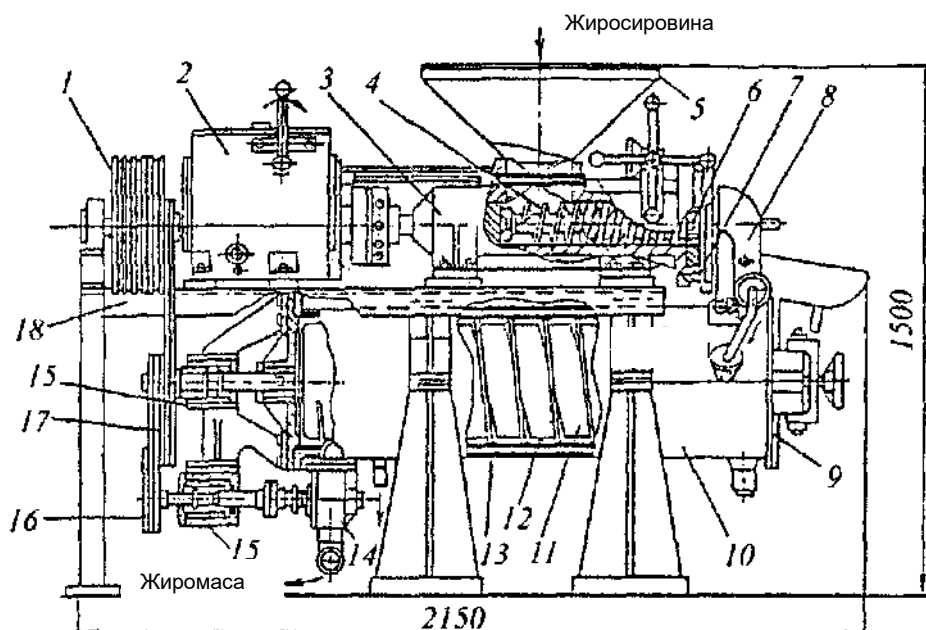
Подрібнювач-розтоплювач установки «Титан»: 1, 16, 17 – клиноремінні передачі; 2 – редуктор, 3 – корпус подрібнювача; 4 – двошнековий насос; 5 – бункер; 6 – решітка; 7 – затяжна гайка; 8 – плоске дно; 9 – передня відкидна кришка; 10 – розтоплювач; 11 – шнековий барабан; 12, 13 – внутрішній і зовнішній корпусу; 14 – насос; 15 – підшипникові опори; 18 – станина
